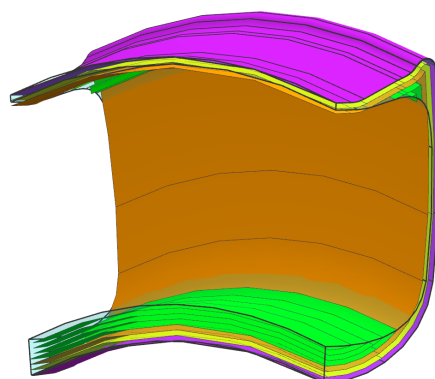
Laminado. Laminado del aro para el ensayo II. (Fuente: Propia)
